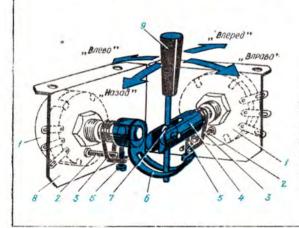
Механизм уп-1 - nepeравления: менные резисторы (R2, R6); 2 -- упоры; 3 -возвратные прижины; 4 — соединительная втулка; 5 — стопорные винты; 6 - поводок;7 — рычаг; 8 — корпус; 9 — ручка управления.
